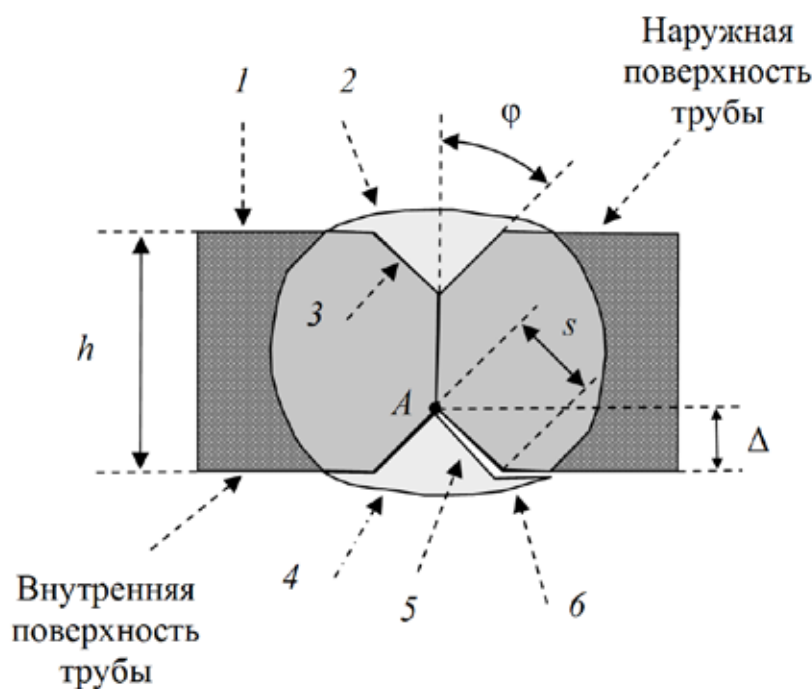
Схема дефекта частичного несплавления сварного шва трубы
